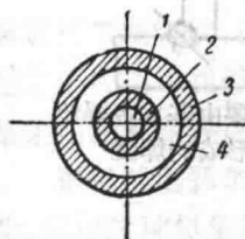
E.M. 庫茲馬克及I.I. 陀洛寧焊条示意图
